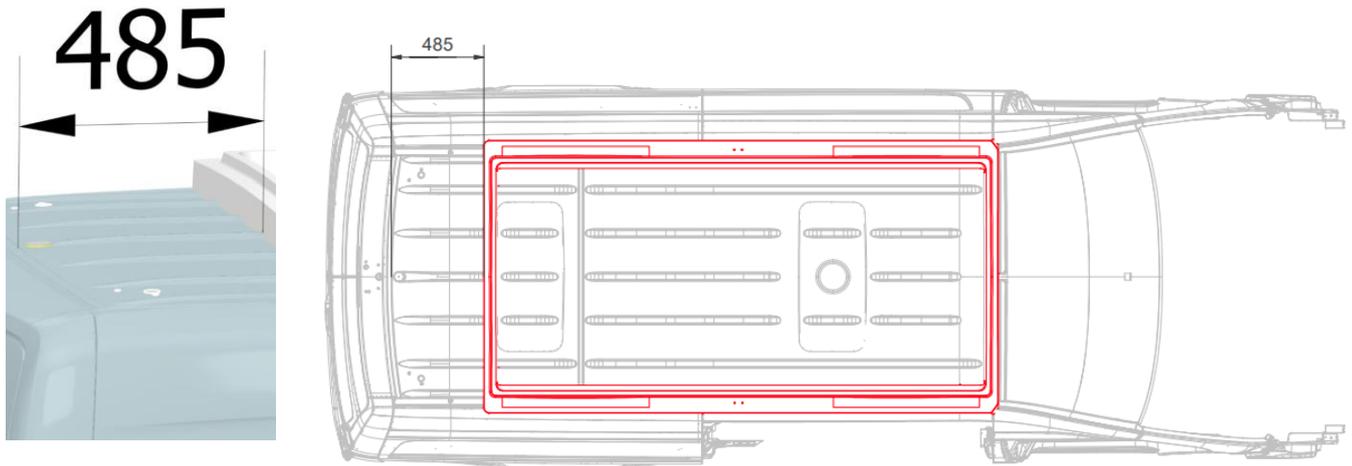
MB Sprinter L2H2 (L = 5932 mm) [G0002136]
